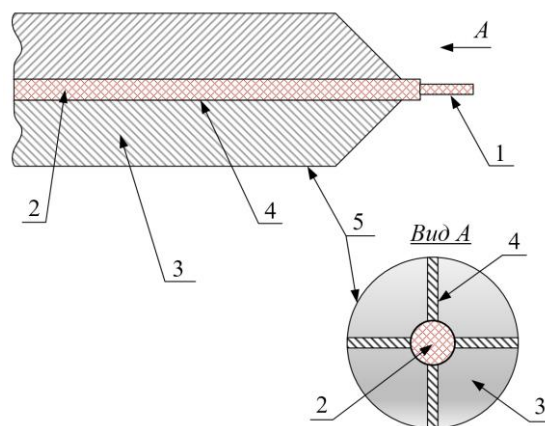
Схема конструкции базового элемента акустического патрона; вид сбоку (а) и с торца (б).
